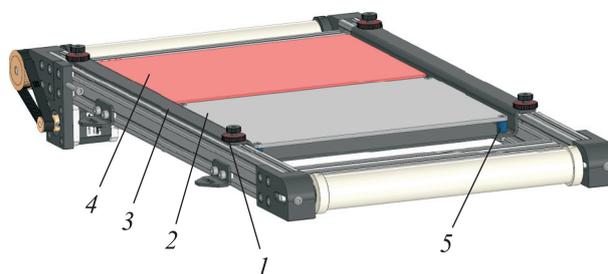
Цифровая сборка конвейерного стола без ленты:
